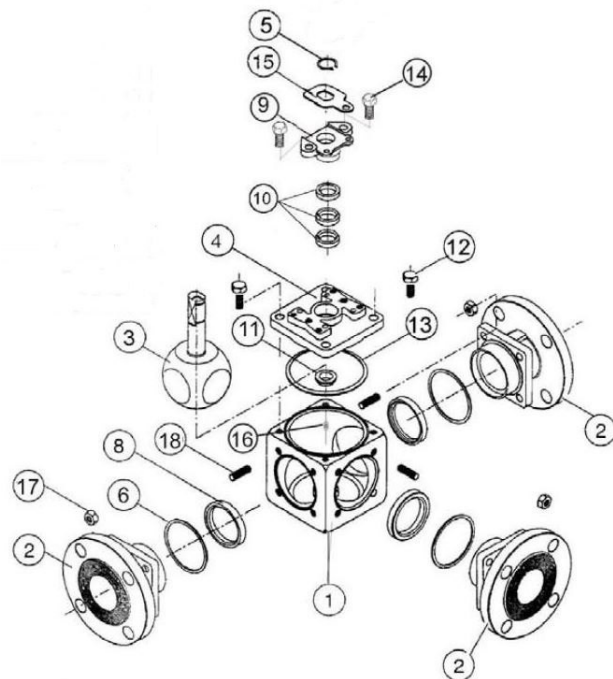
Bauteilliste Kugelhahn DN50...200 DUKE-F
